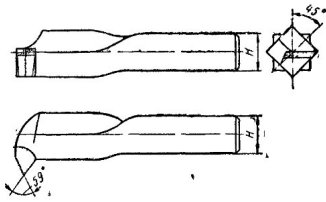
Резьбовой резец для нарезания внутренней резьбы конструкции В. К. Семанского
